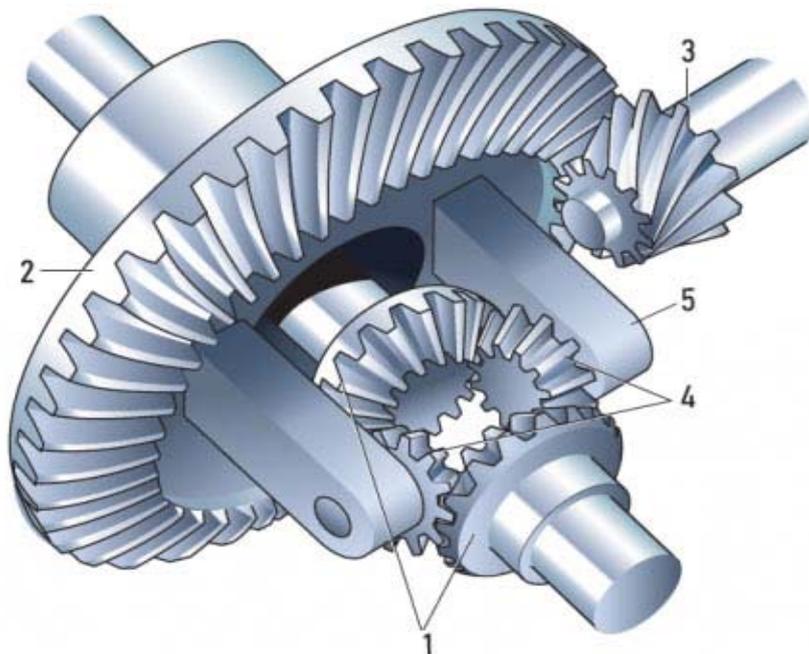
Устройство дифференциала: 1 – шестерни полуосей; 2 – ведомая шестерня главной передачи; 3 – ведущая шестерня главной передачи; 4 – сателлиты; 5 – корпус.
